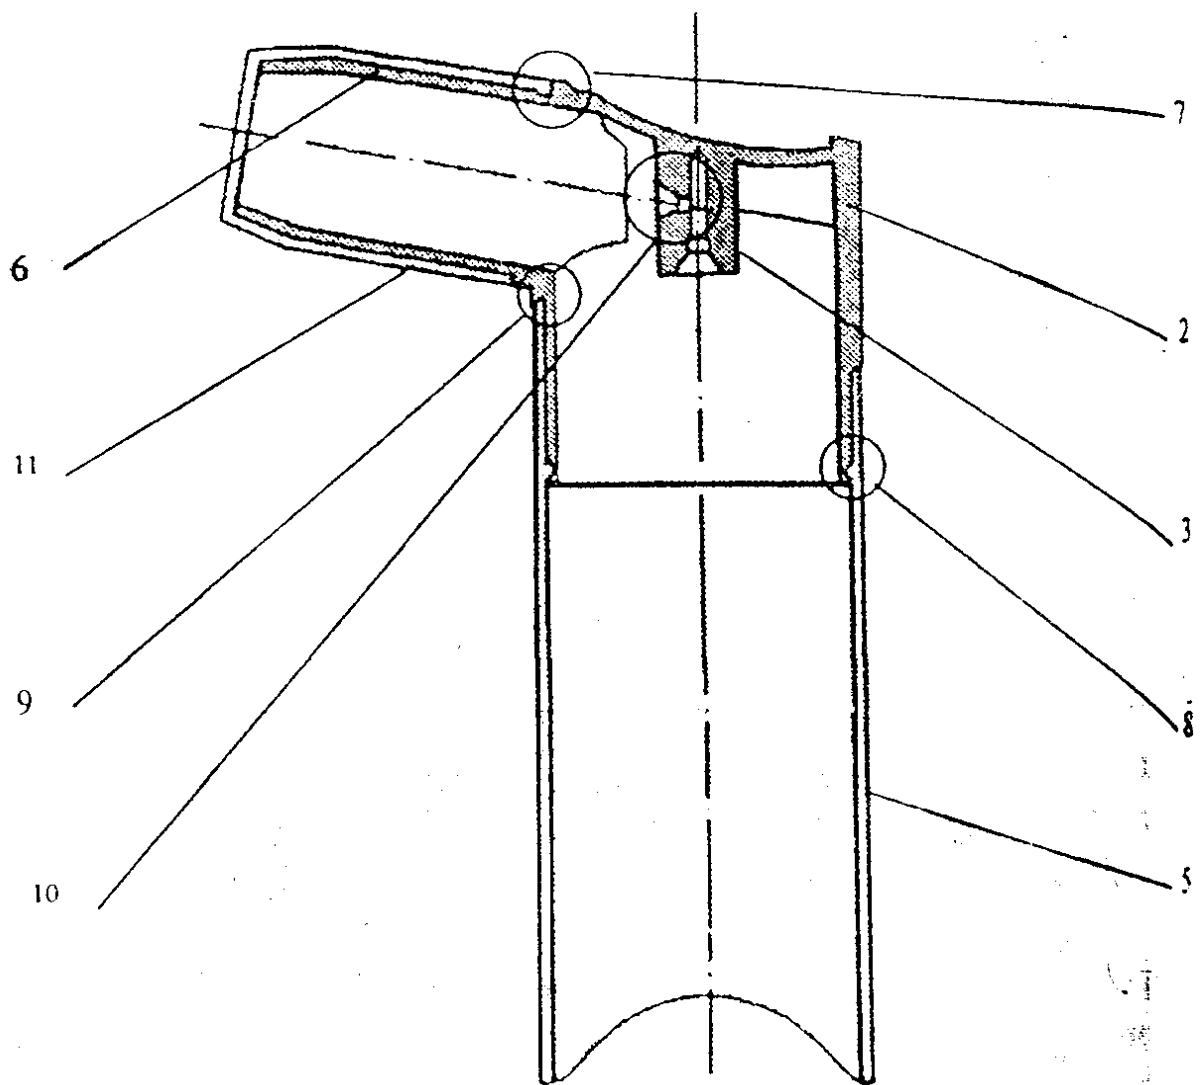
Схема закупорювального засобу для дозованого аерозолю: 1 – ковпачок; 2 – корпус кришки; 3 – розпилювач; 4 – сопло розпилювача; 5 - напрямний кожух; 6 – направляюча потоку; 7 – фіксатор №1; 8 – фіксатор №2; 9 – фіксатор №3.
